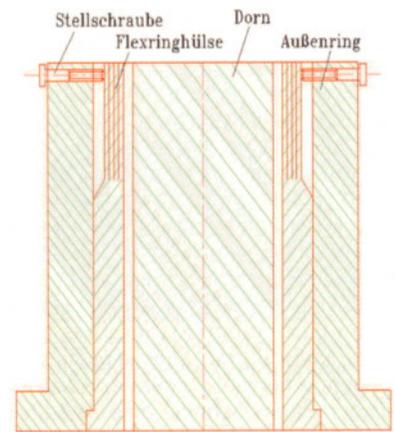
Skizze der parallelen Austragszone eines Werkzeugs mit integrierter Flexringhülse.
